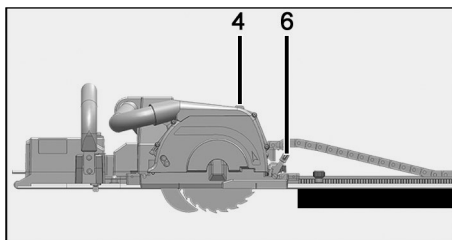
Colocar la máquina sobre la pieza de trabajo para el corte longitudinal
